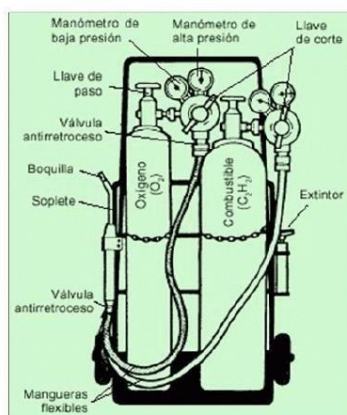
Equipo de Soldadura de Oxicorte
